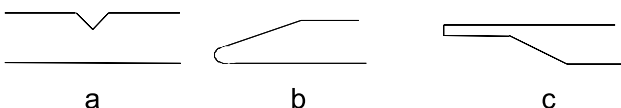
Ángulos relacionados con tolerancias. Fuente: Bralla, James, Handbook of Product Design for Manufacturing. A practical guide to low cost production, Cap. 5.3, "Fundición en molde con revestimiento", R.J. Spinosa, Ed. McGraw-Hill, 1993.
